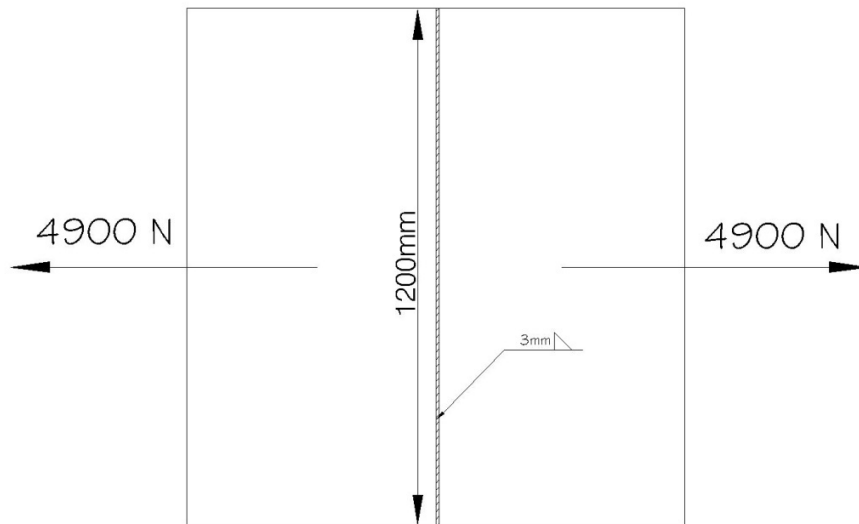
Detalle 3 de soldadura para tapas del cilindro
